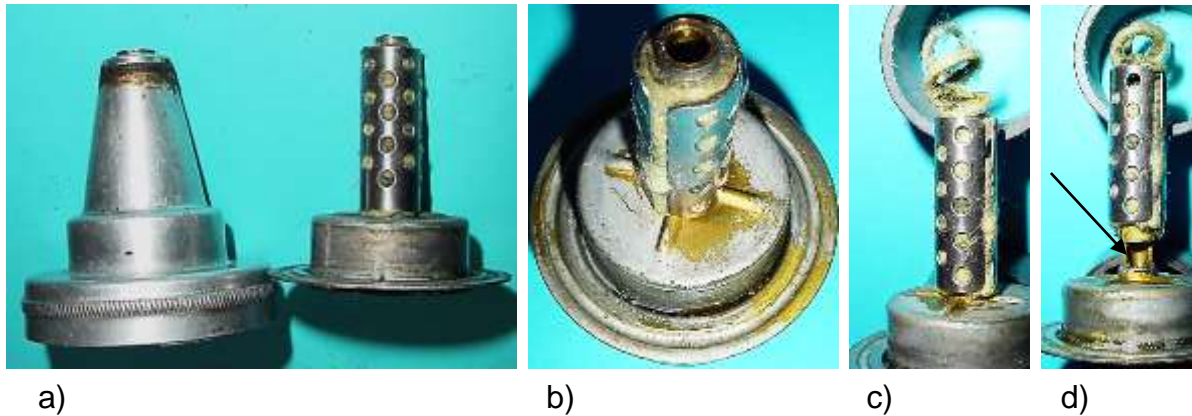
Lagerhals: a) Lagerhals und Lagerhalseinsatz, b) Lagerrohr mit Lager-
